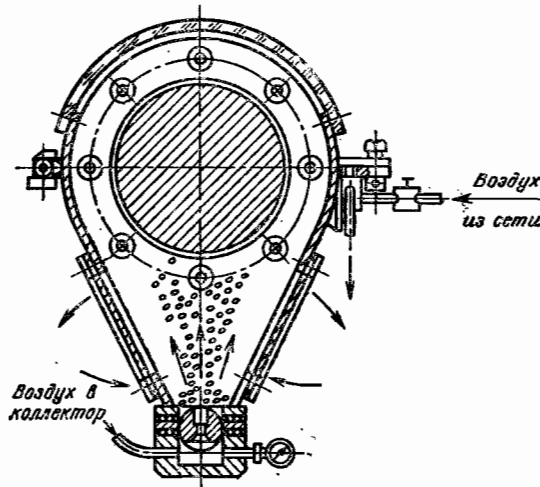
Схема камеры для пневмодинамической обработки деталей
